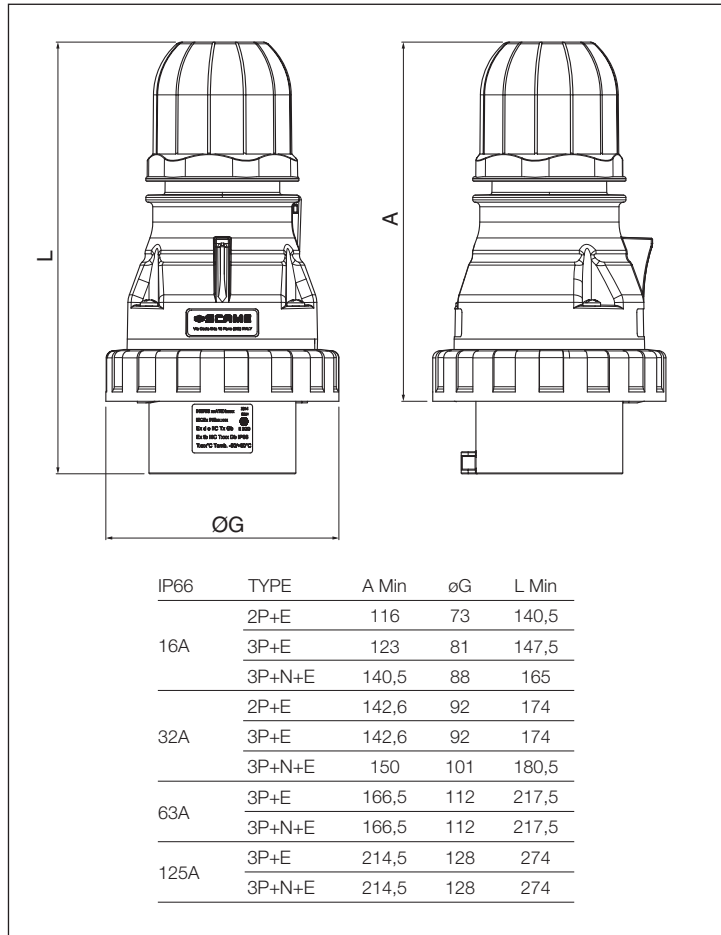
IT: Disegno tecnico della spina. / EN: Technical drawing of the plug. / FR: Schéma technique de la fiche. / ES: Diseño técnico de la clavija. / RU: Чертеж штепсельной вилки.
